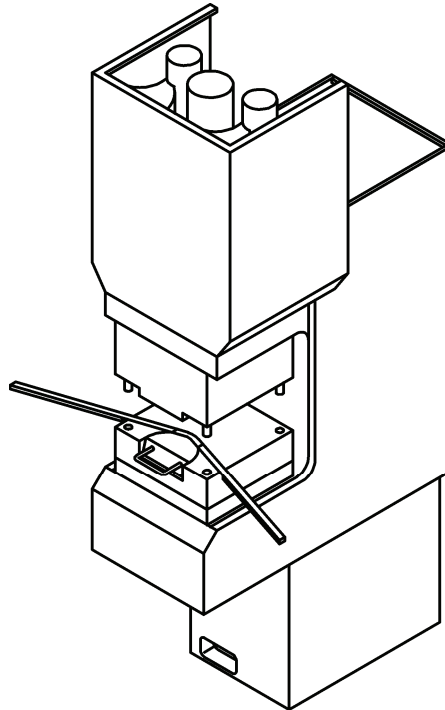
Beispiel einer Eckenanspritzmaschine, dargestellt ohne Schutzeinrichtungen des Werkzeugbereichs
